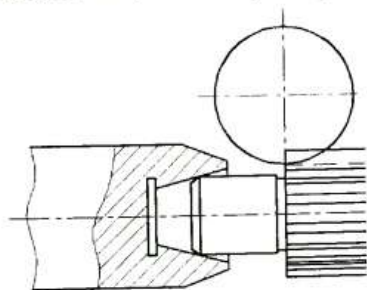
Схема наскрізного фрезерування шліців із застосуванням оправки зі зворотним конусом
